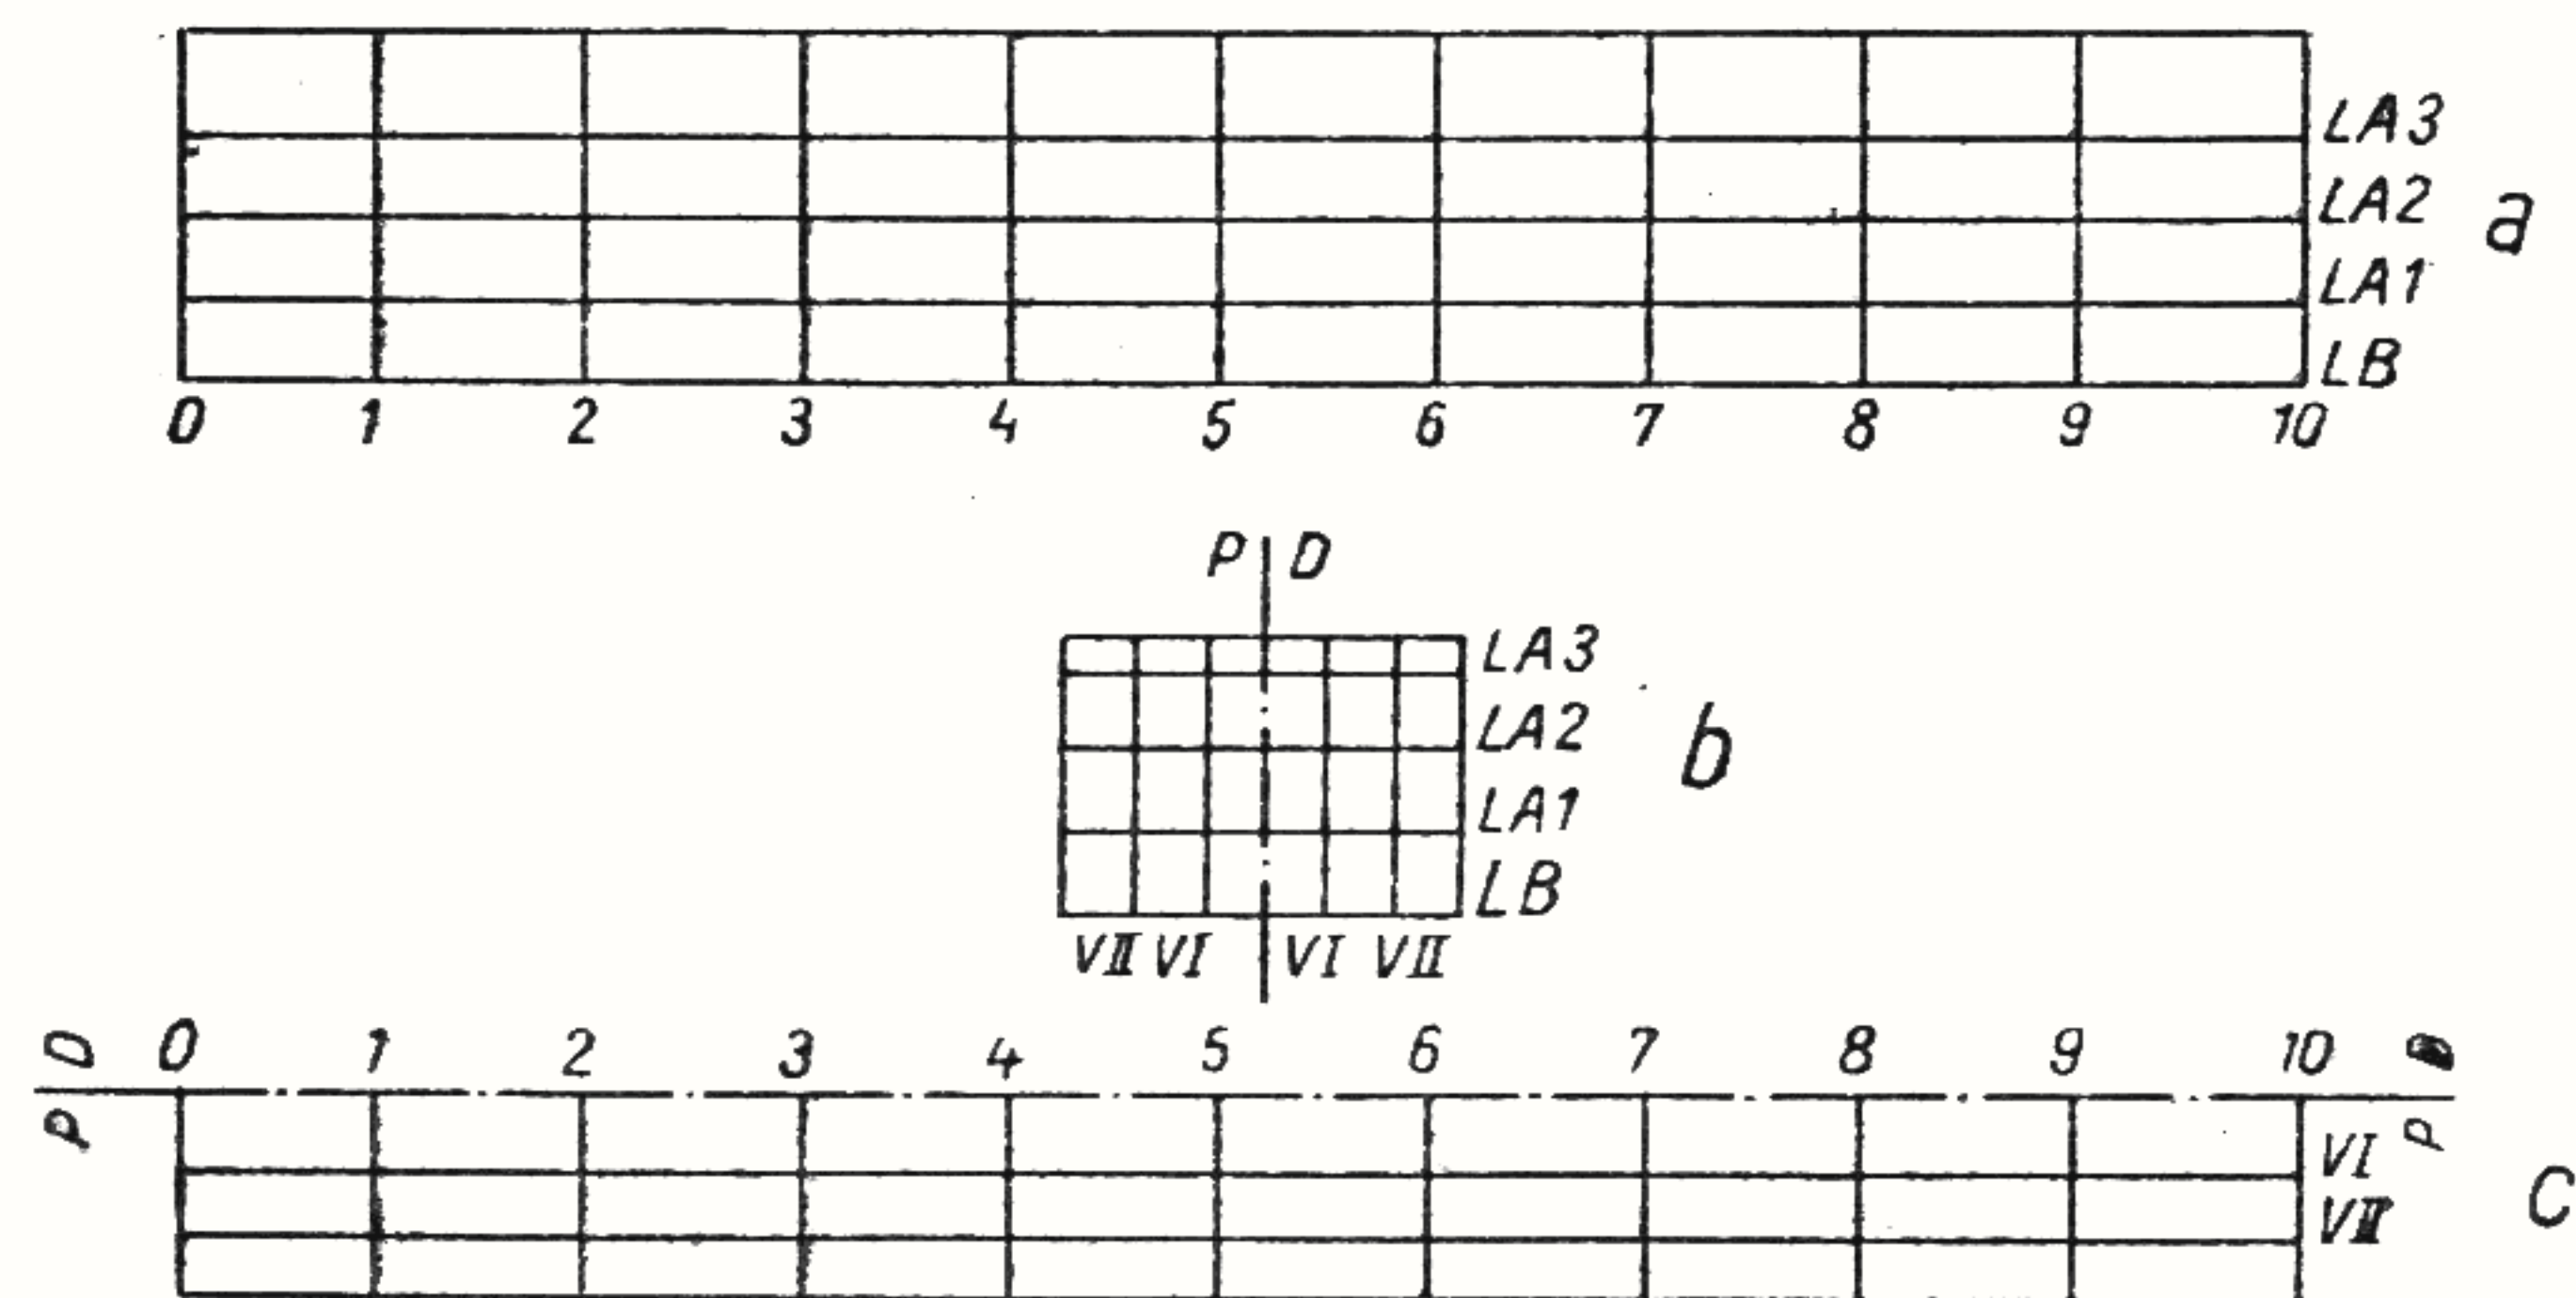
Caroiajul planului de forme: a) planul vertical longitudinal; b) planul vertical transversal; c) planul orizontal.
